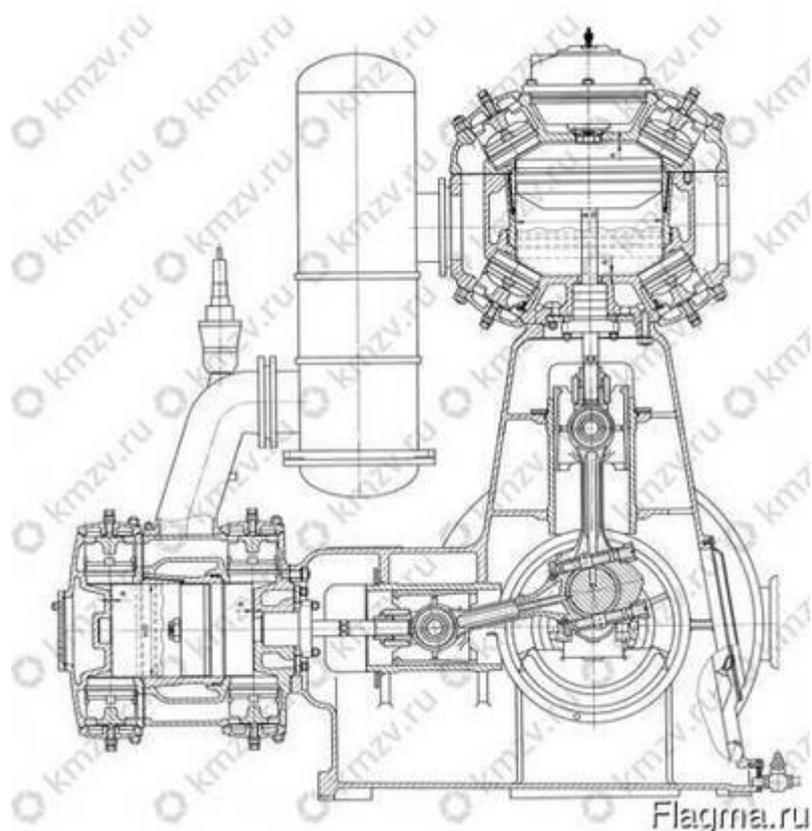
Общий вид углового компрессора (305ВП-30/8).
